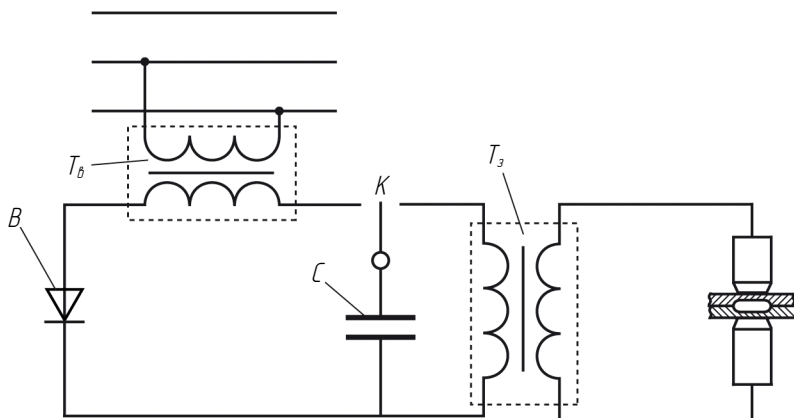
Схема точкового зварювання на конденсаторній машині
